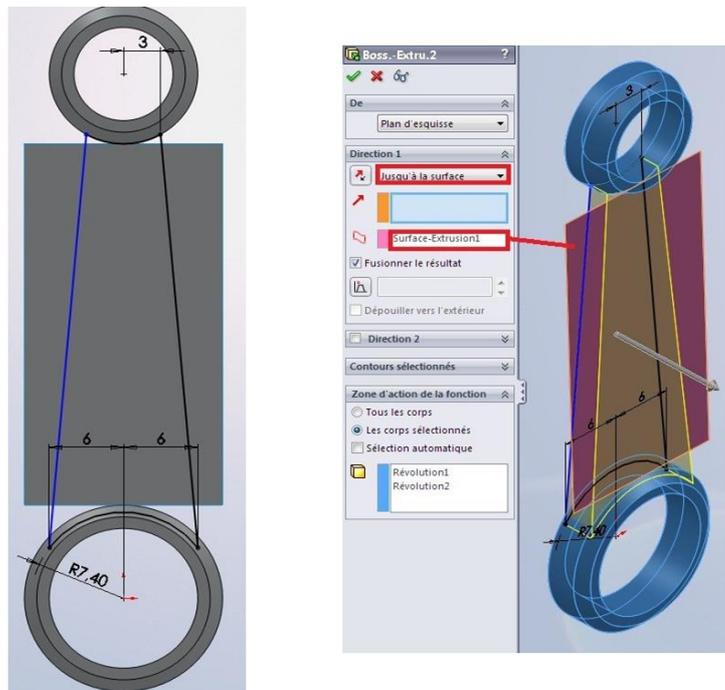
Esquisse sur le plan de face et fonction de l'extrusion.
